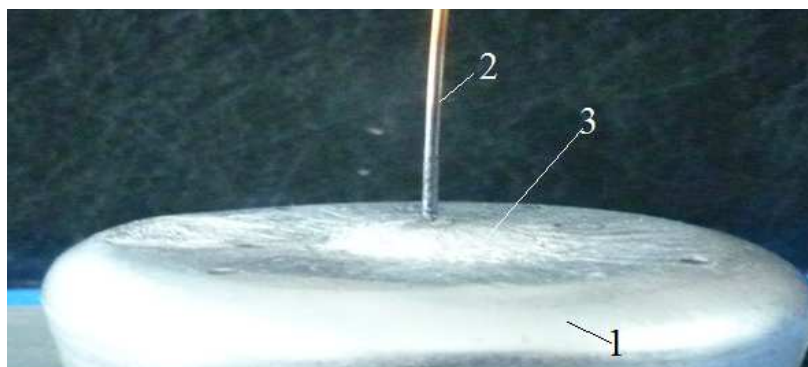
Образец расплава алюминия. 1.Образец отливки.2-коронирующий электрод. 3. Конус, замкнувший разрядный промежуток.
